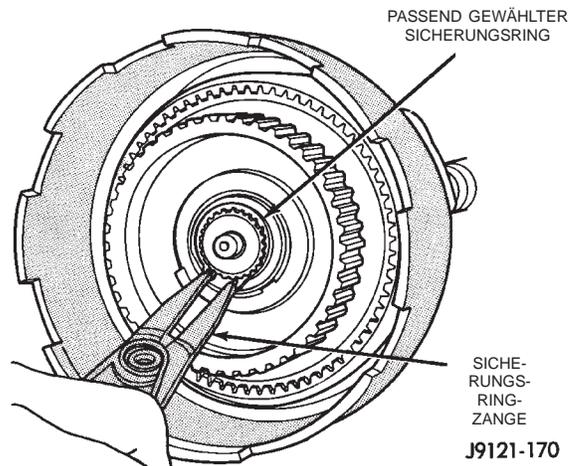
Passend gewählten Sicherungsring für Planetenradsätze montieren
